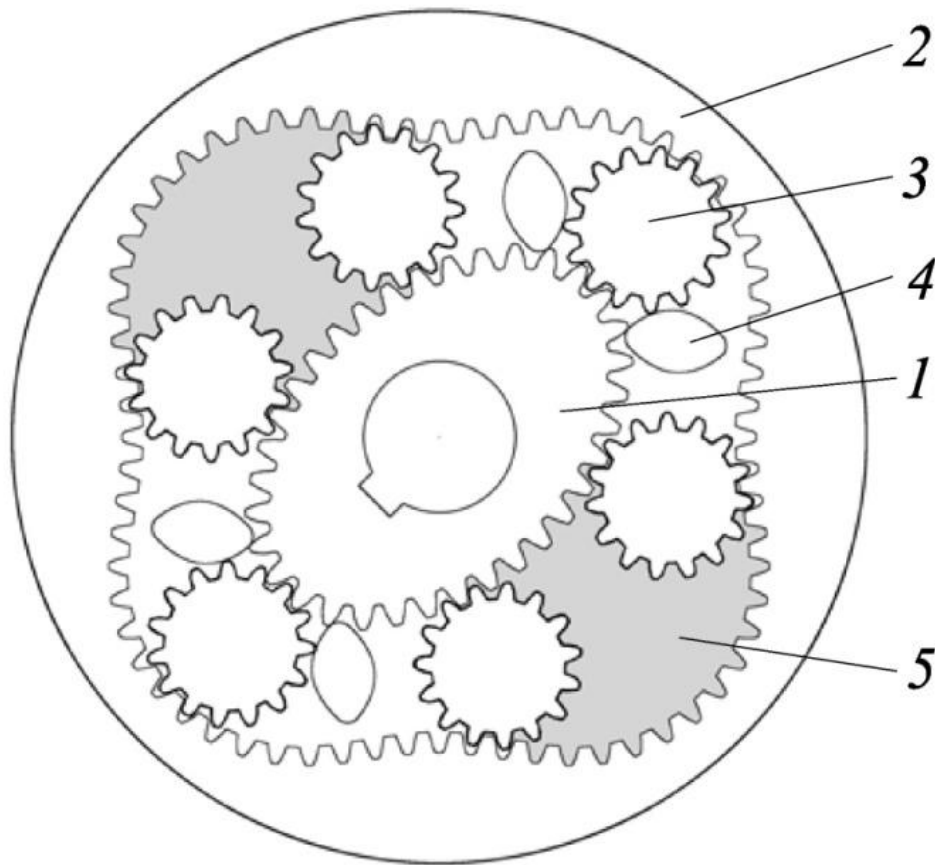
Схема РГМ: 1,2 - солнечные колеса с внешними и внутренними зубьями; 3 - сателлиты; 4 - каналы для рабочей жидкости; 5 - рабочие камеры
